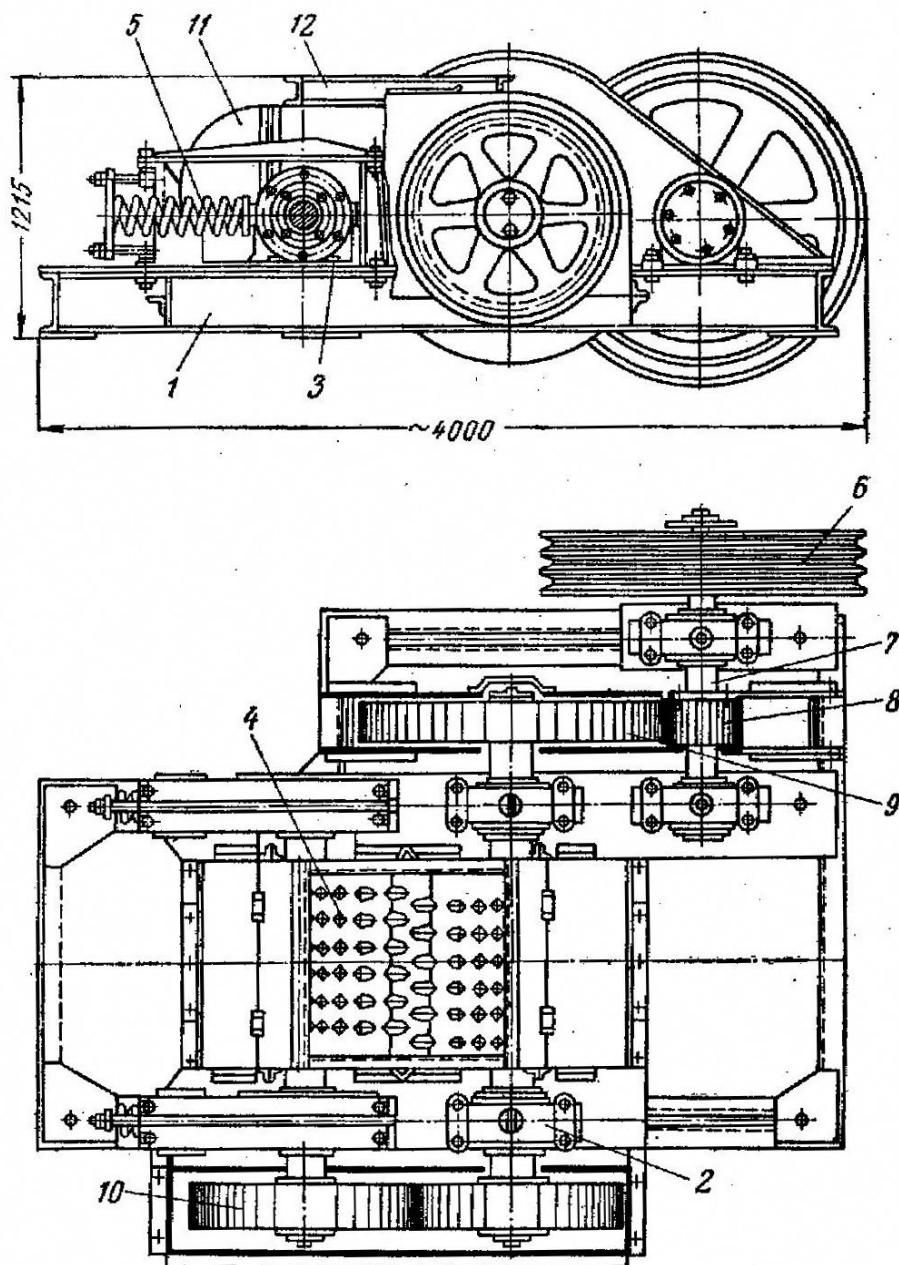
Дробилка двухвалковая зубчатая ДДЗ-4 [2]:
